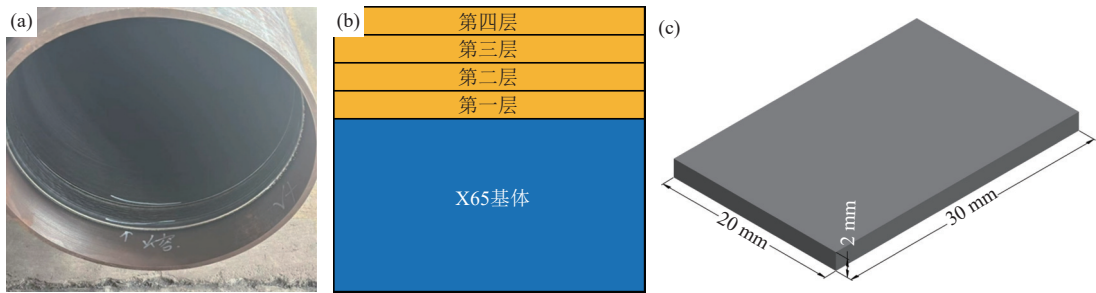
X65/Inconel625 双金属复合管外观形貌 (a)、堆焊结构示意图 (b) 和腐蚀实验试样尺寸 (c)
